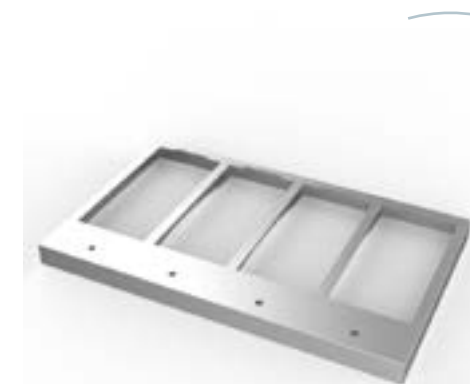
Estrutura final metálica para a integração de 4 elementos para colocação na categoria estrutura
